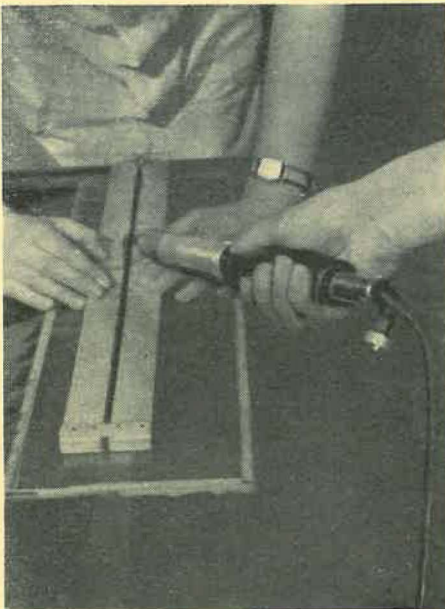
Technik des Schweißens einer Polyäthylenfolie
